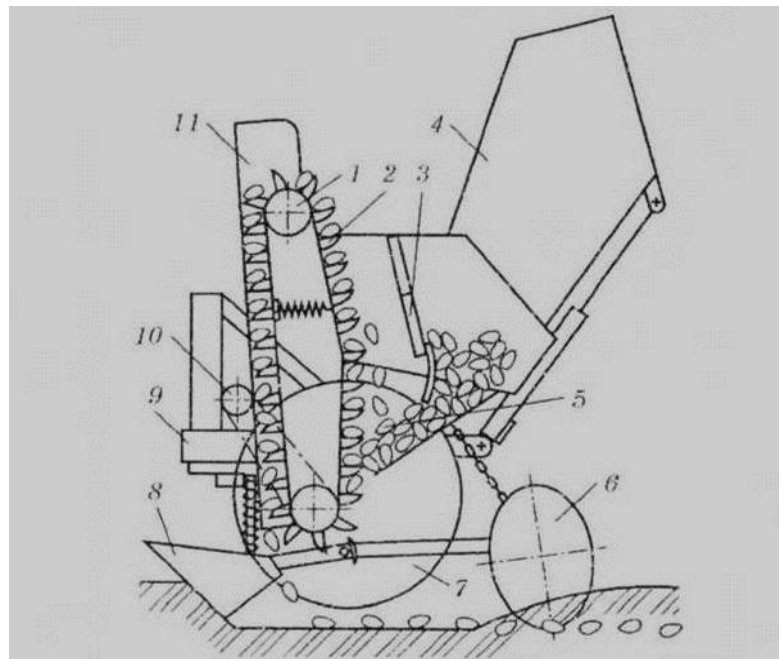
Картоплесаджалка Л-202: 1 – садильний апарат; 2 – ложечка; 3 – бункер; 4 – заслінка; 5 – живильний ківш; 6 – дисковий загортач; 7 – опорно-привідне колесо; 8 – сошник; 9 – рама; 10 – механізм приводу; 11 - кожух
